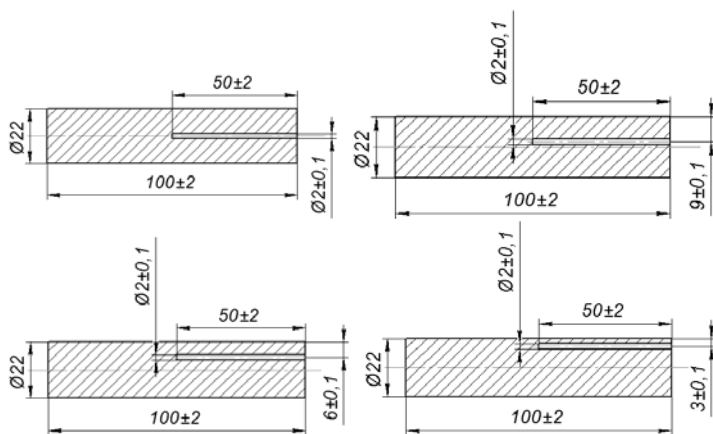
Эскизы исследуемых образцов прутков с боковыми цилиндрическими сверлениями
